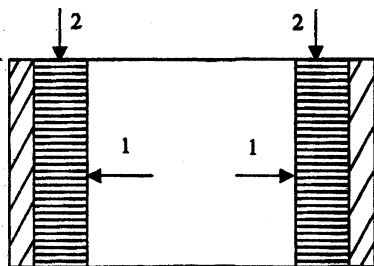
Подшипник скольжения самосмазывающийся: 1 – торцевое направление резания; 2 – поперечное направление резания
